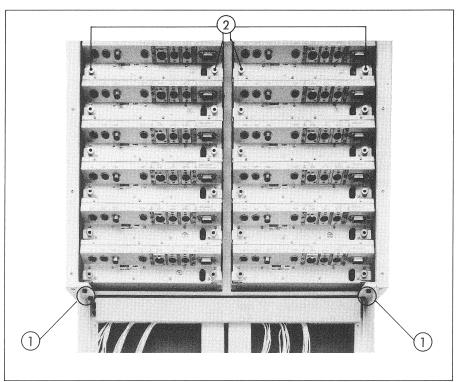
Befestigungsschrauben des Rahmens und der Einschübe
